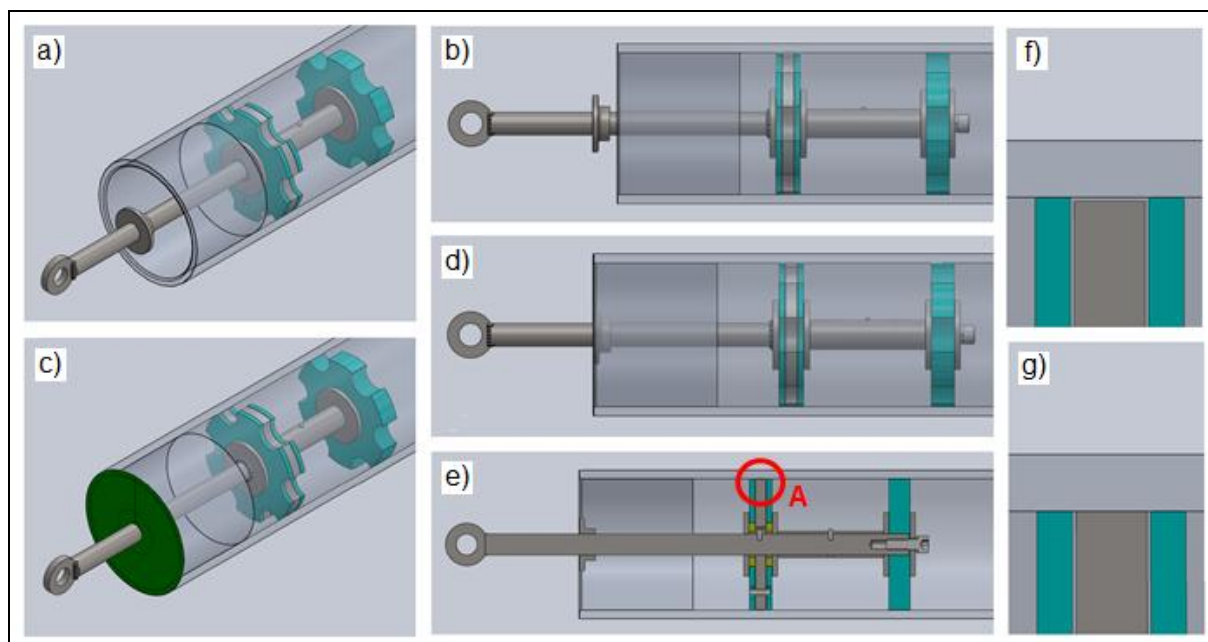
Závěsný trn s pružným zemnicím mechanismem – závěsný trn. a), b) c) základní pohledy, d) řez, e) pružný mechanismus.
